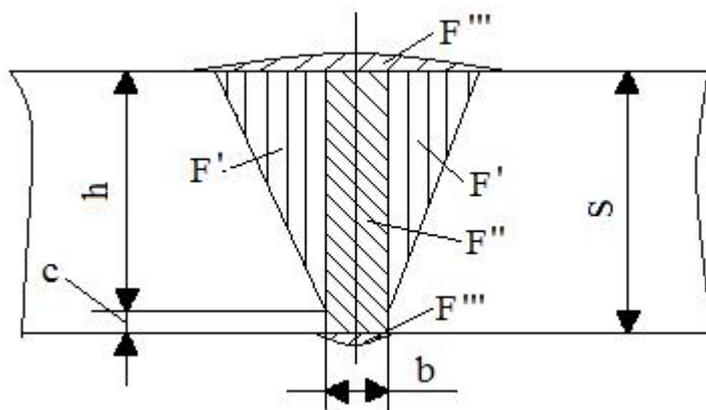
Форма поперечного сечения сварного соединения типа С17 или С21
